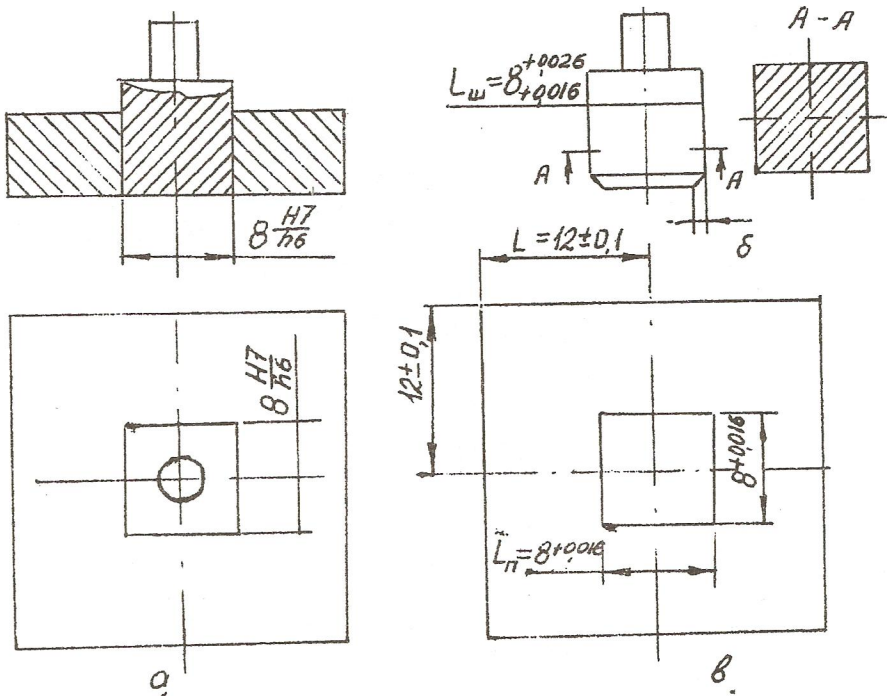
Пример варианта задания: а - чертеж сборочной единицы; б - чертеж штифта; в - чертеж основания
